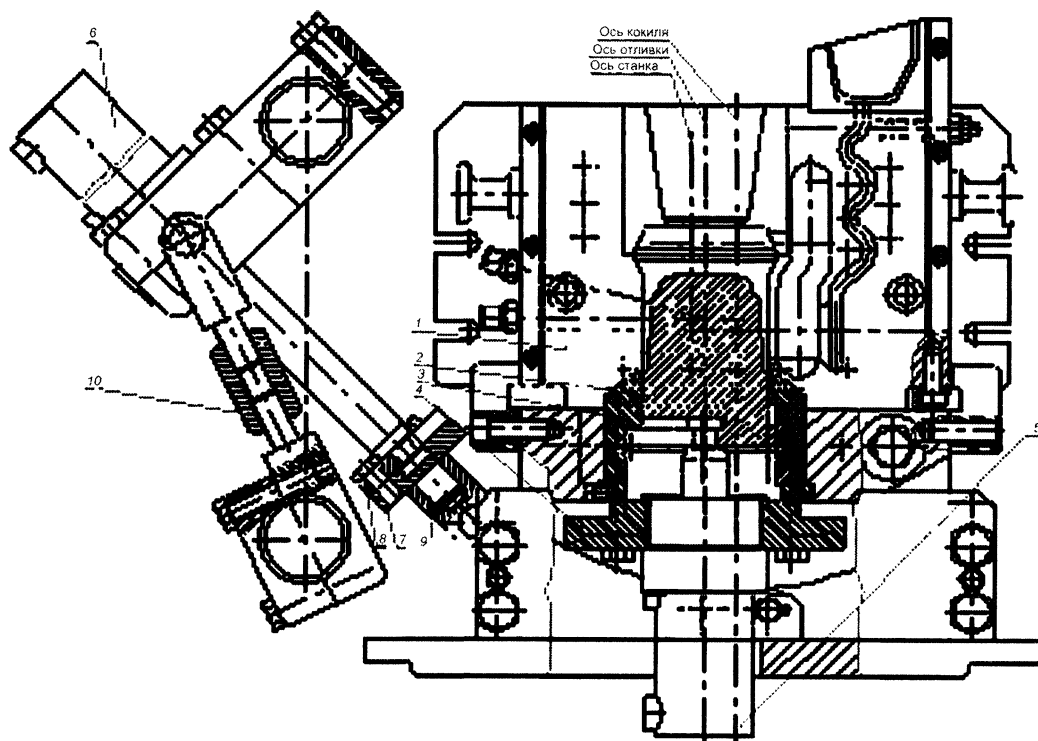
Металлический кокиль для производства поршней с нирезистовой вставкой под верхнее компрессионное кольцо для высокофорсированных двигателей: 1 – матрица правая (матрица левая не показана); 2 – стержень; 3 – втулка; 4 – плата; 5 – гидроцилиндр установки стержня (ход 50 мм); 6 – гидроцилиндр поворота кокиля (ход 200 мм); 7 – тяга; 8 – замок; 9 – тяга-муфта; 10 – муфта
